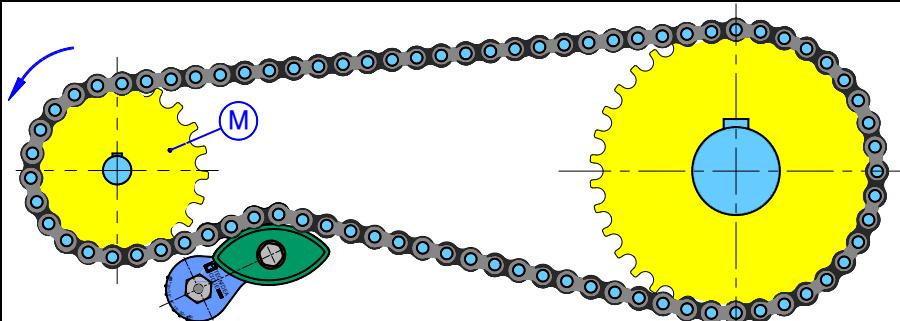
Montaggio corretto con azionamento dall'interno.
